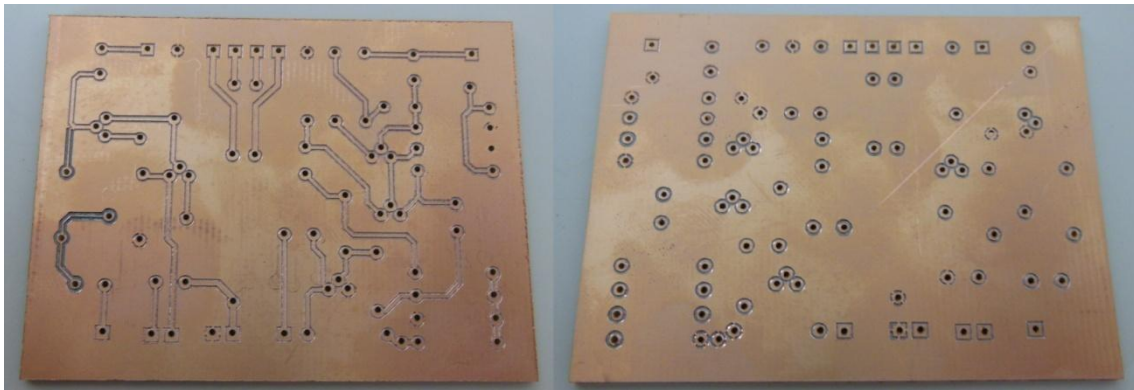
PCB DISEÑADA SIN LOS COMPONENTES SOLDADOS
